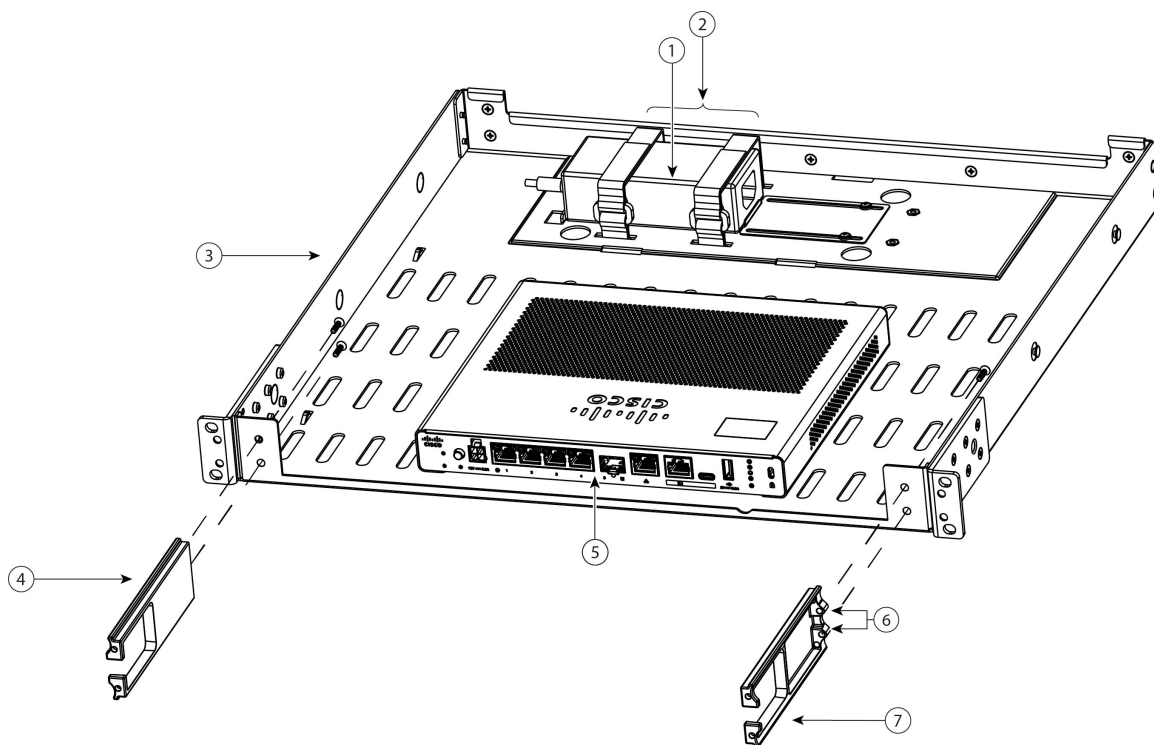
Installazione dello chassis sulla mensola per montaggio in rack
